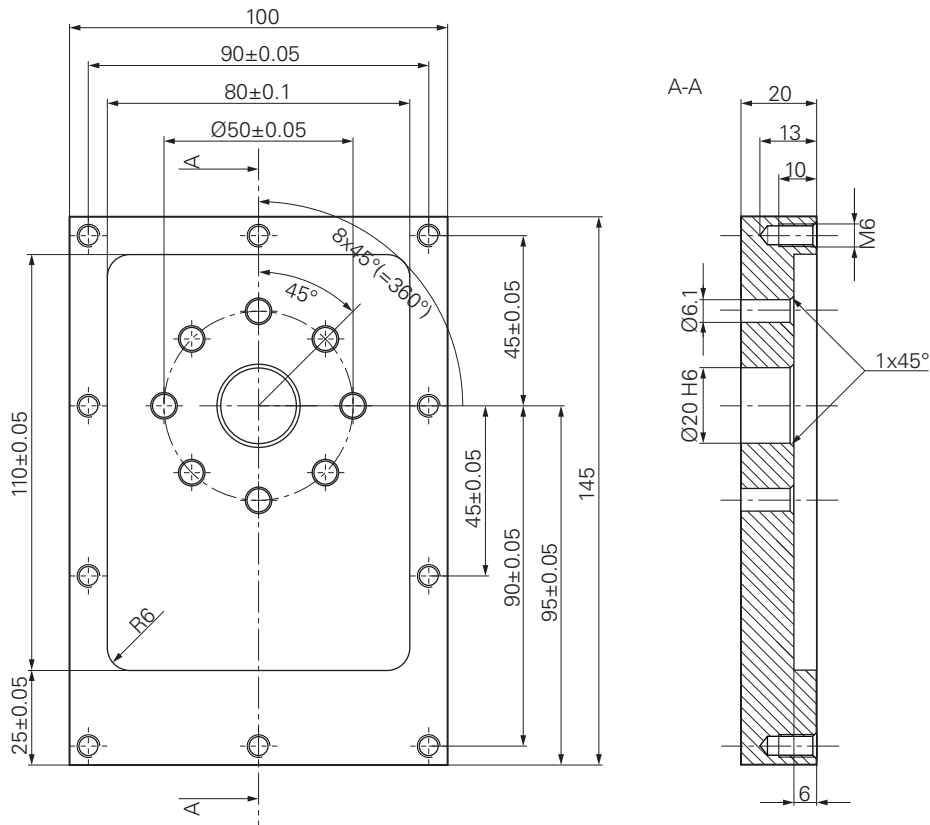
Peça de trabalho de exemplo – Desenho Técnico
